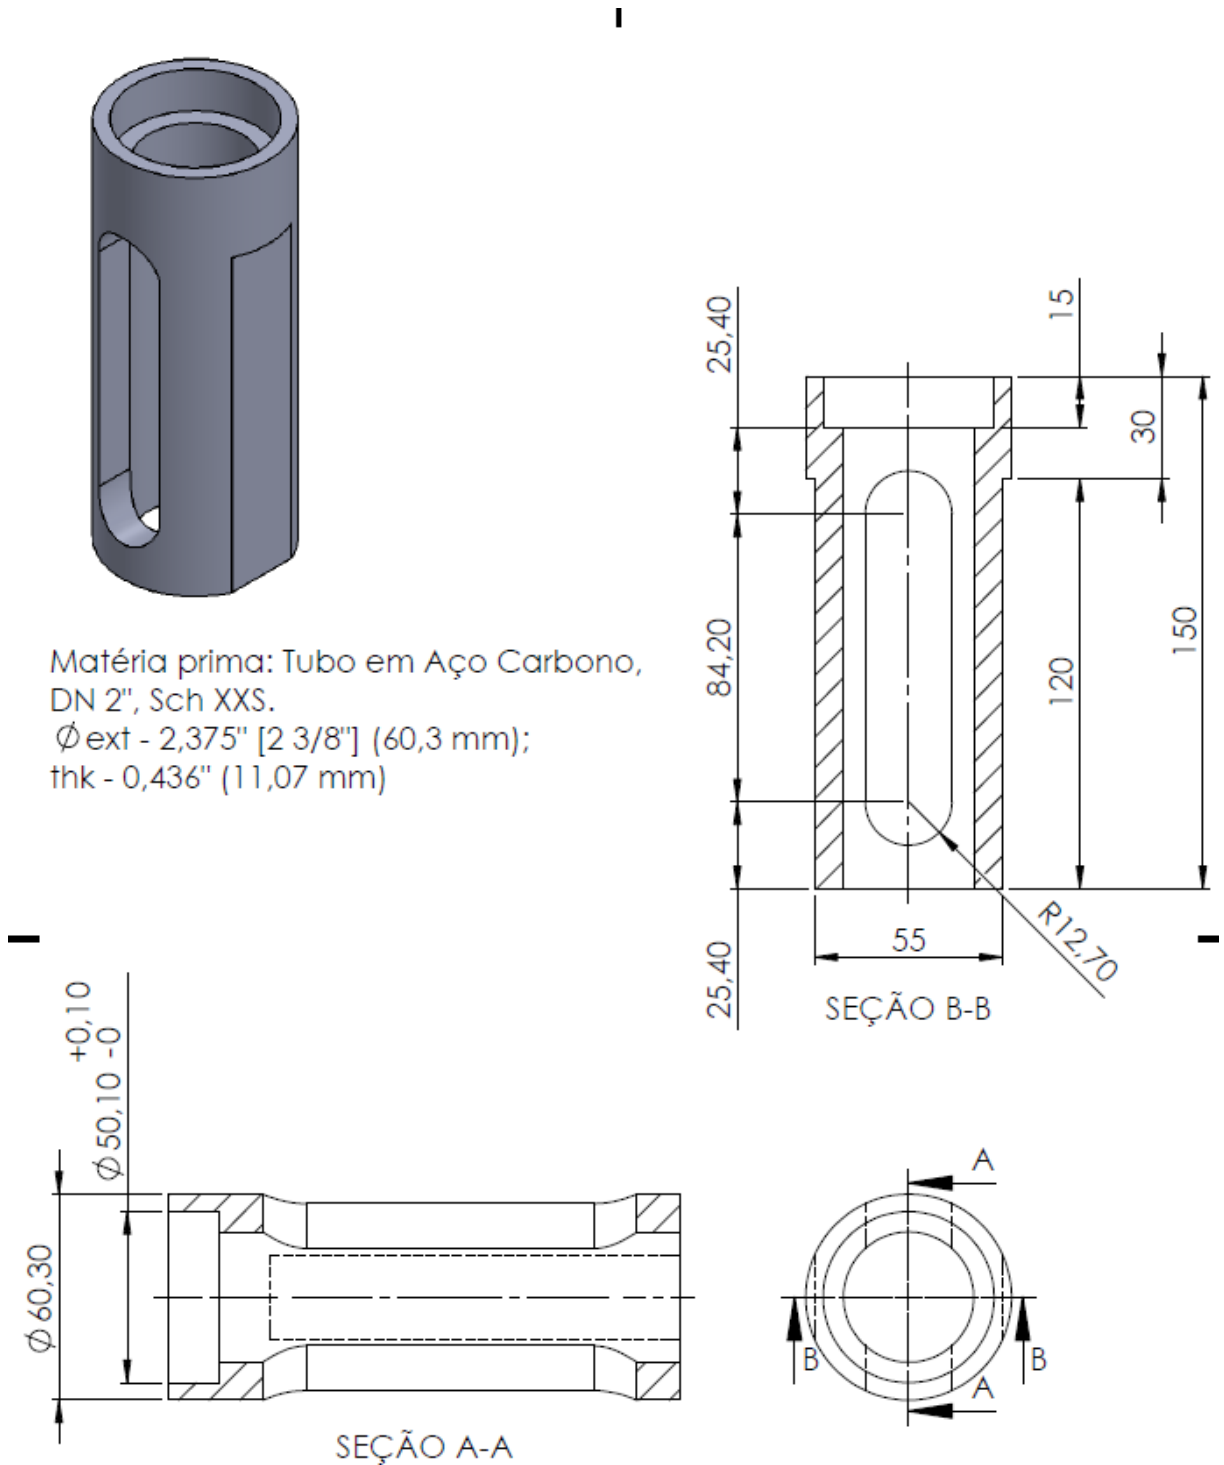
Detalhamento da sede superior do dispositivo de teste para execução do ensaio SPT com base no guia CWA 15627.
